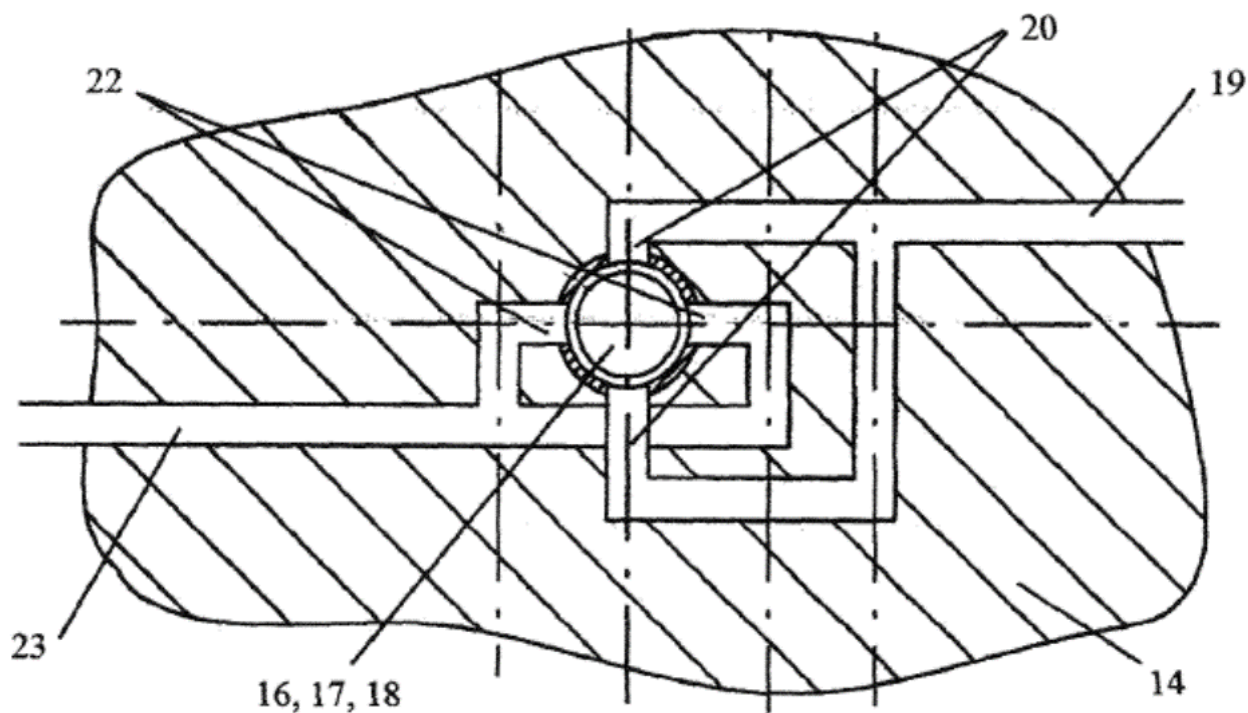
Поперечний переріз корпусу ПНВТ
